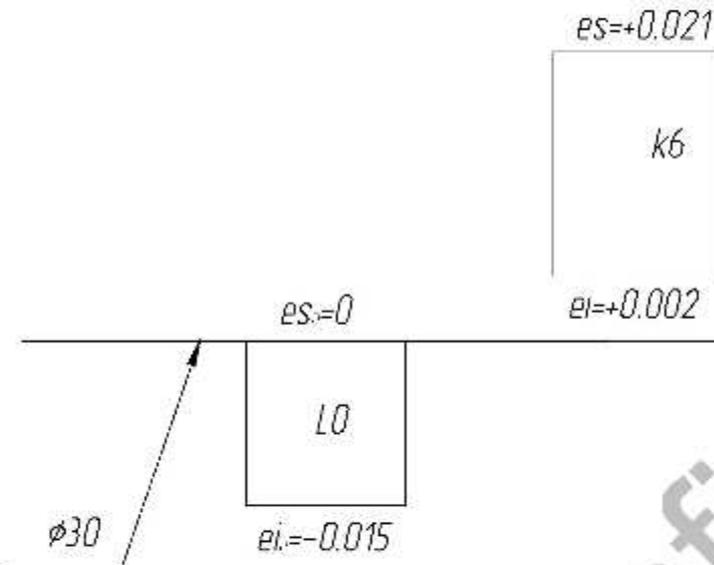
Схема расположения полей допусков деталей соединения
